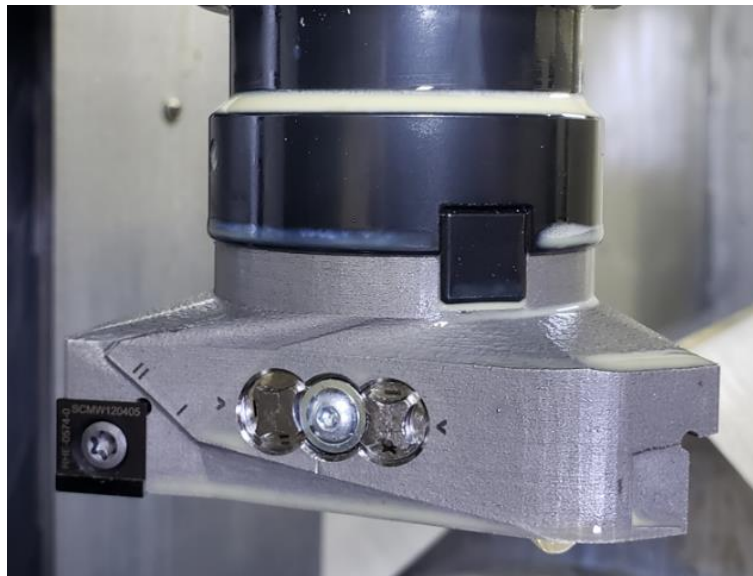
Vytištěný a obrobený nástroj QCA 1.0
